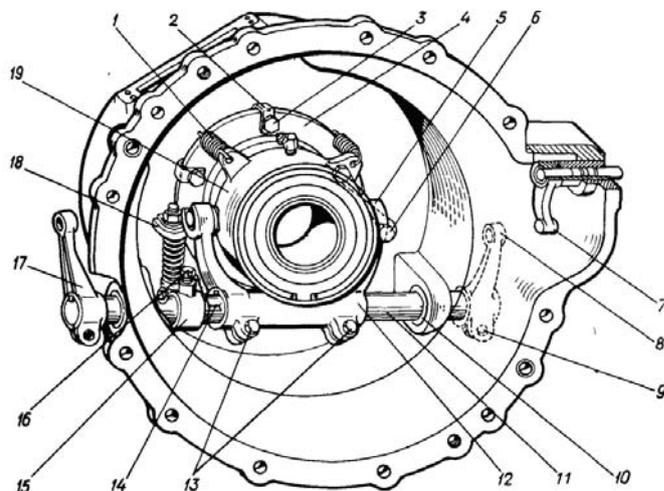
Разборка корпуса: 1 — пружина; 2 — шайба; 3, 6, 9, 13, 16 — болт; 4 — направляющая; 5, 14 — проволока; 7, 8, 17 — рычаг; 10 — втулка; 11 — вал; 12 — вилка; 15 — муфта серги; 18 — колодка тормозка; 19 — корпус выжимного подшипника
